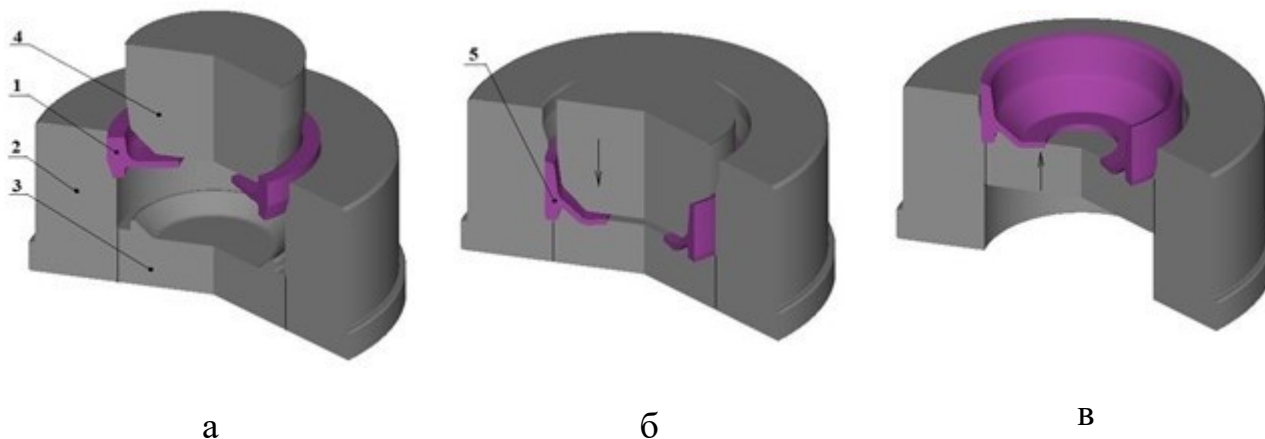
Розрахункові розташування деформуючого інструменту і заготовки показані в розрізі: а- розташування на початку, б- розташування в кінці, в- розташування після виштовхування
